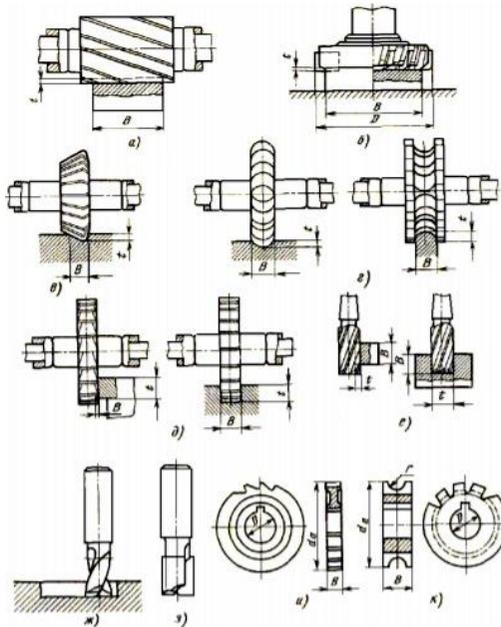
Типы фрез и обрабатываемых поверхностей
